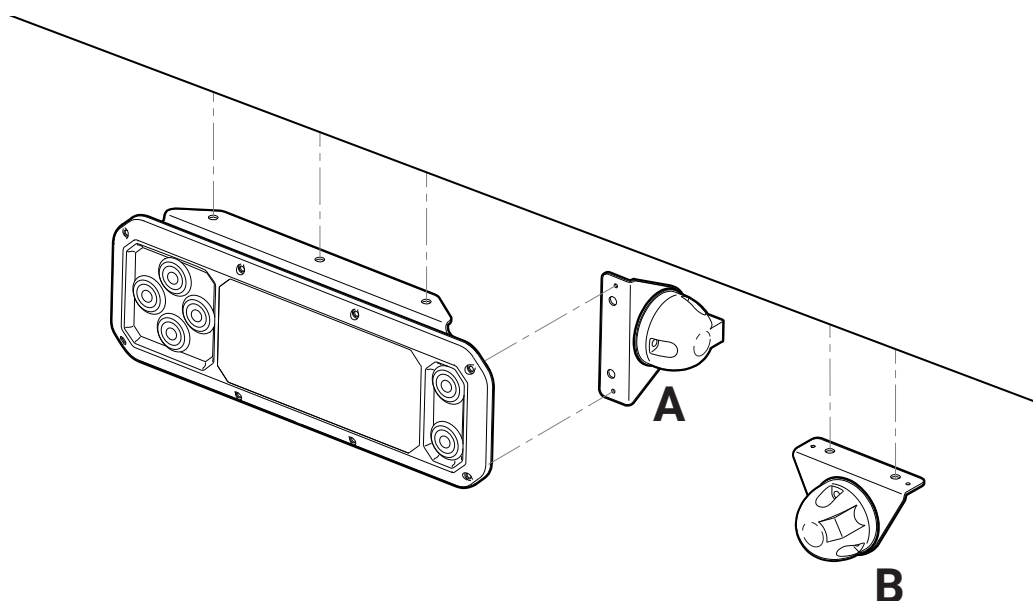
Montaje del actuador CD19 y del conector para actuador portátil
